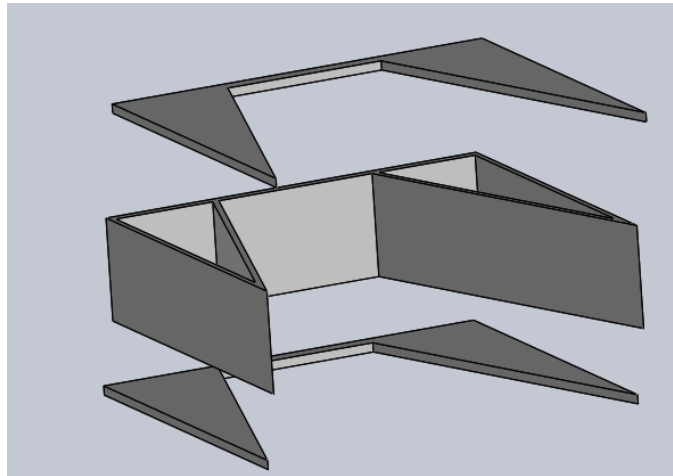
Vista explosionada del subensamblaje cajón. [2]
